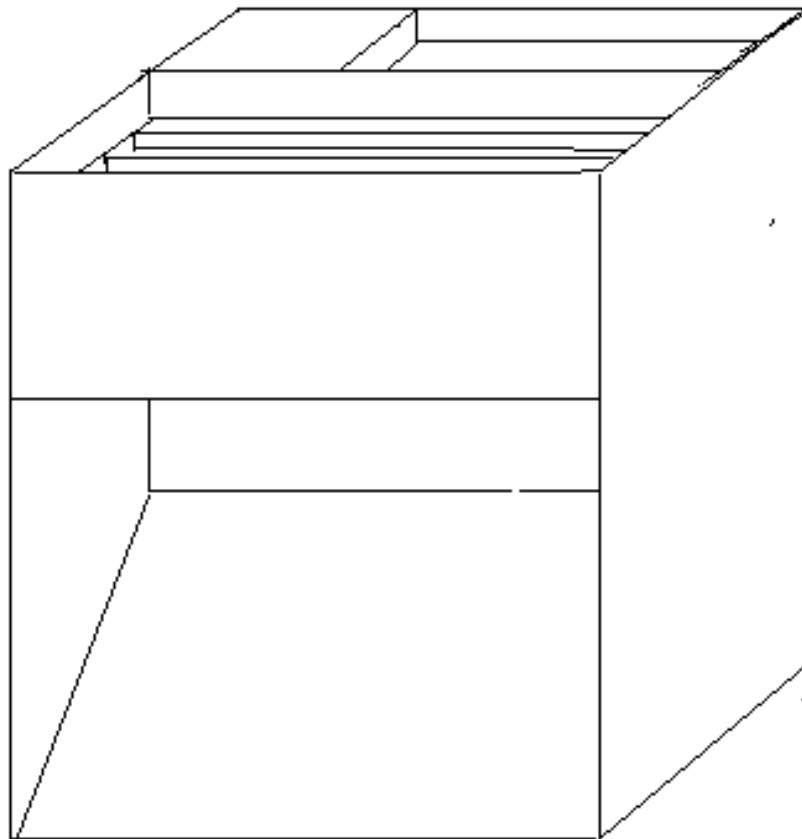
Mesa propuesta para procesos de soldadura.
